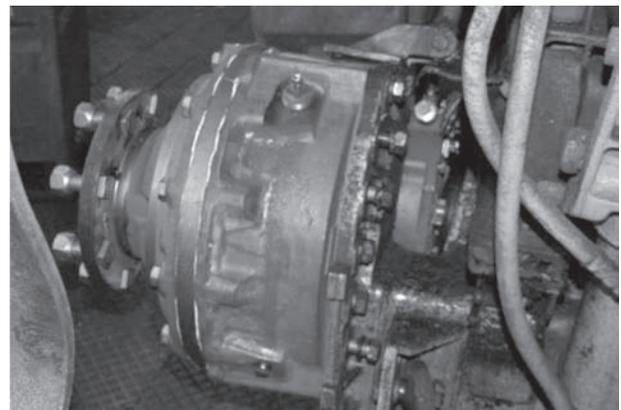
Бортовой редуктор с эпициклической шестерней из ВЧТГ
